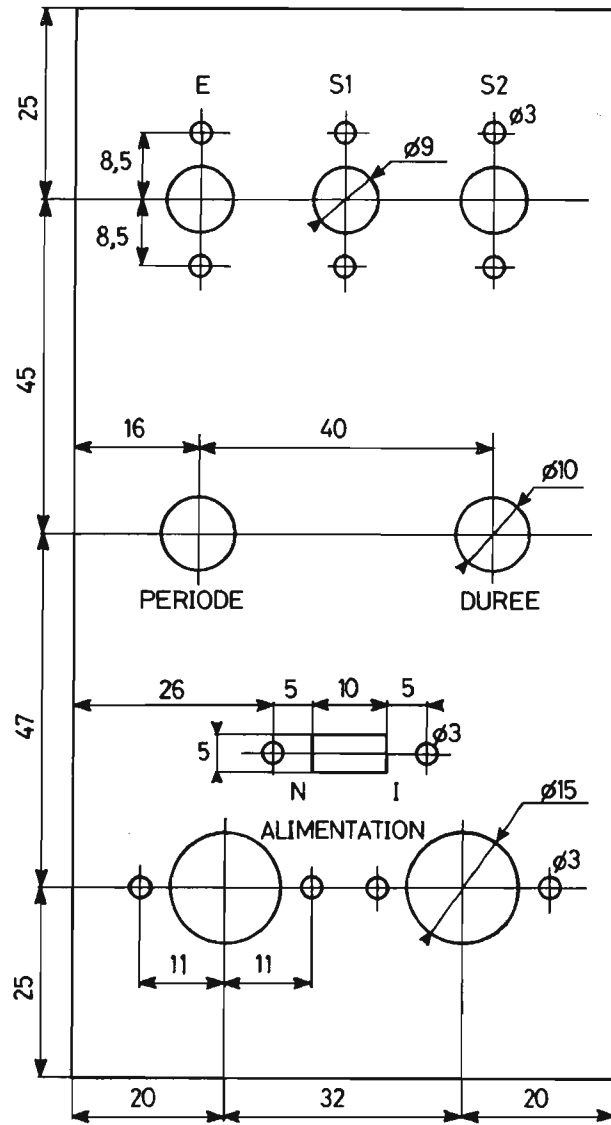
a. et 13 b. - Plan de perçage de la face avant du générateur aléatoire et plan de perçage du fond du boîtier.
